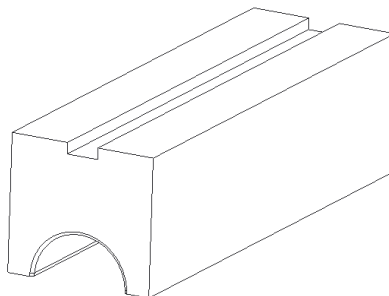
pressure tool disegnato con il software PTC Creo.
